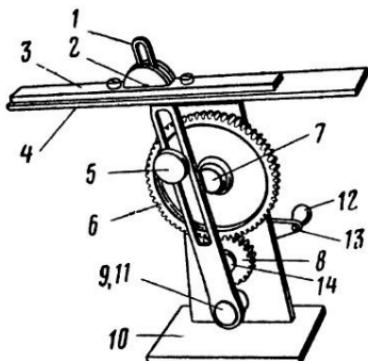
Модель привода попечечно-строгального станка: 1 — кулиса; 2 — шпилька; 3 — «ползун»; 4 — «станина»; 5 — «камень» кулисы; 6 — ведомое зубчатое колесо («маховое»); 7 — ось; 8 — ведущее зубчатое колесо; 9 — винт крепления кулисы; 10 — основание; 11 — ось кулисы; 12 — ручка; 13 — рычаг ручки; 14 — вал привода.
